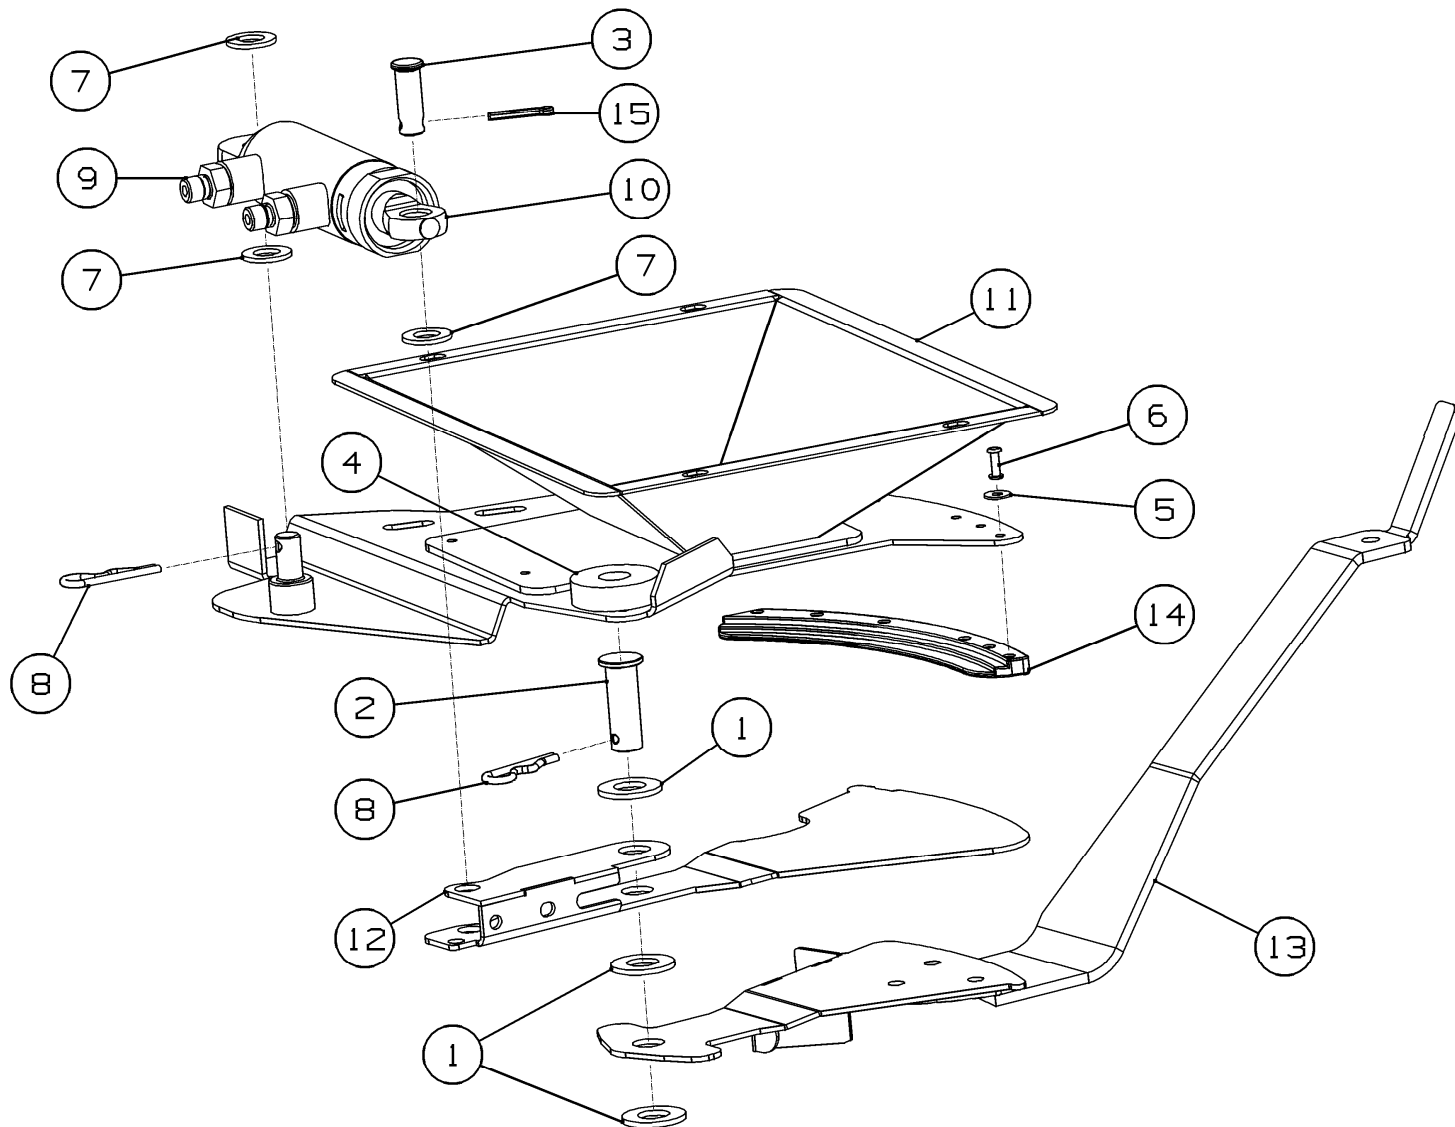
Механизм регулировки высева - PA-900.60.00.000 и PA-900.60.00.000-01
